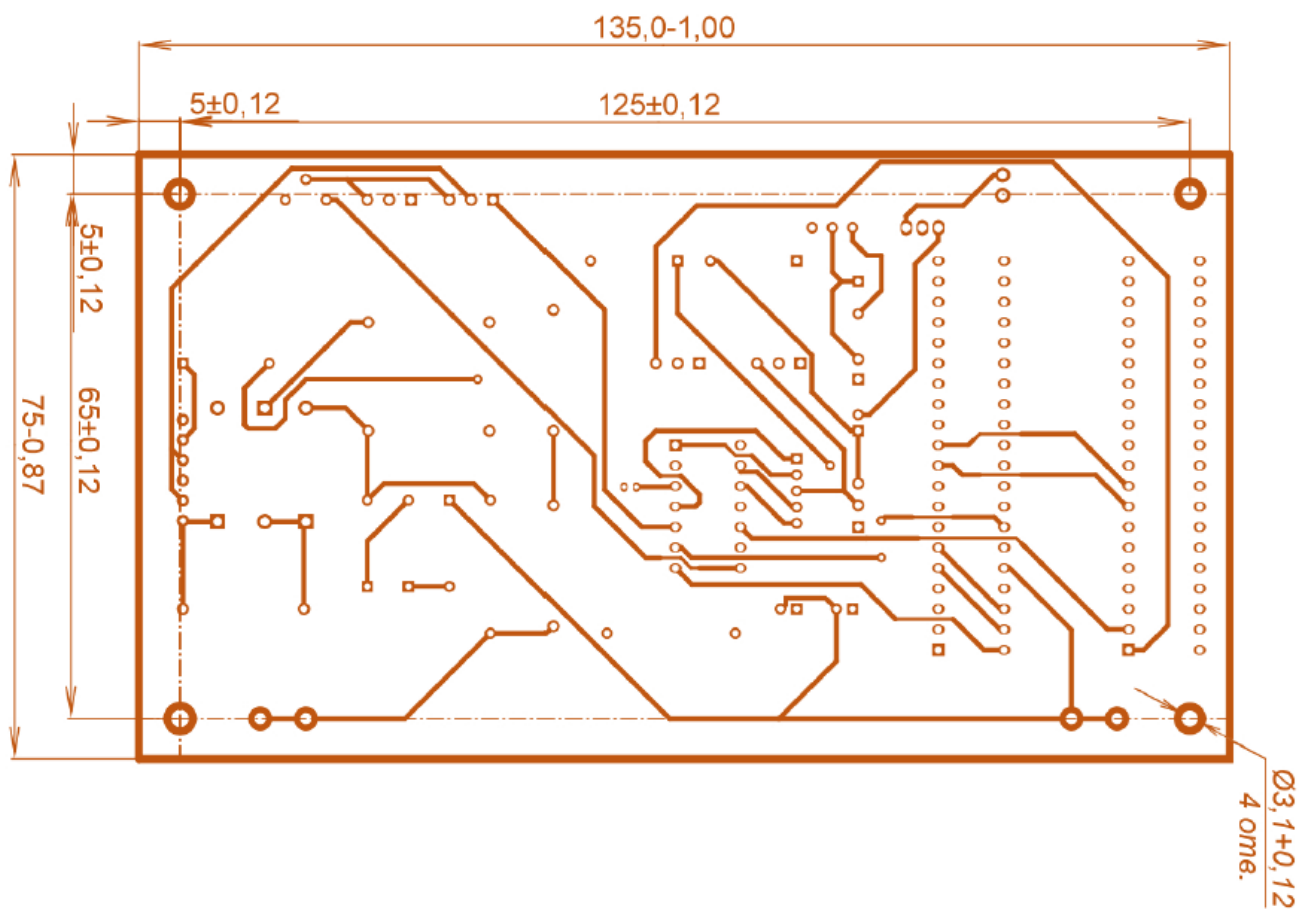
Розроблений у P-CAD макет друкованої плати пристрою вимірювання радіації на базі лічильника J305
